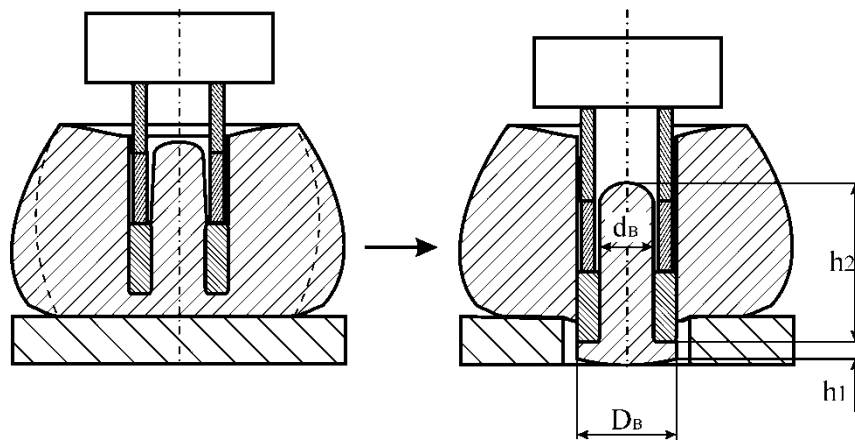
Прошивання заготовки пустотілим прошивнем
